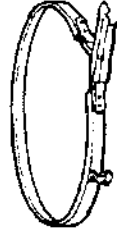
Detalle del cierre con mecanismo de palanca, visto por dentro
